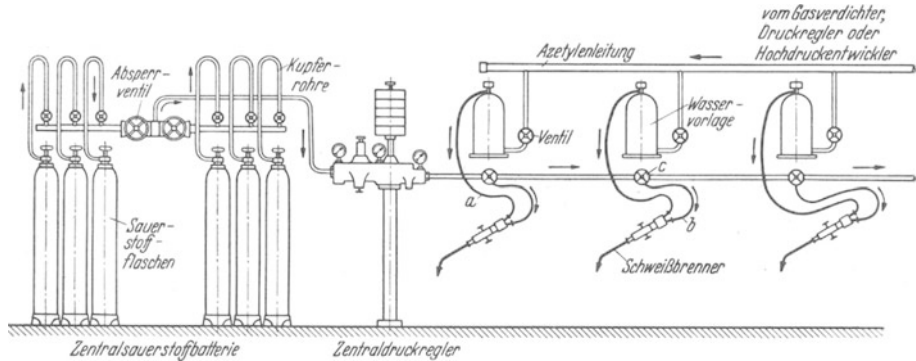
Konstantdruck-Schweißanlage.
